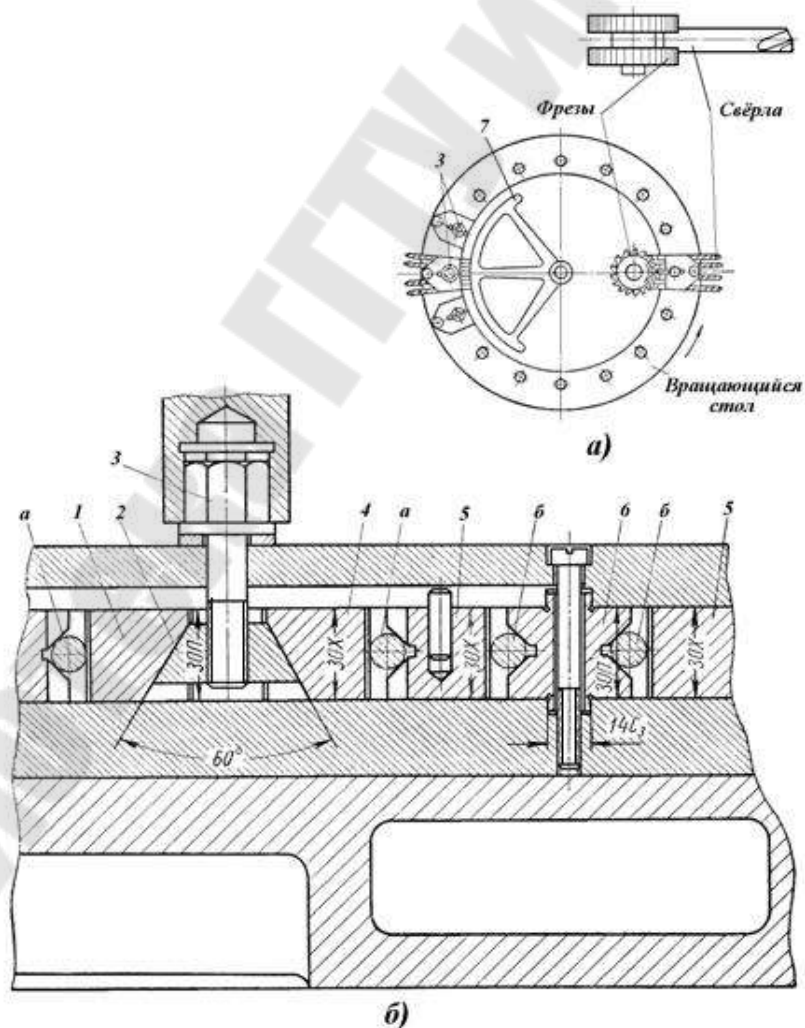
Эскиз приспособления для фрезерования лапок хвостового инструмента
